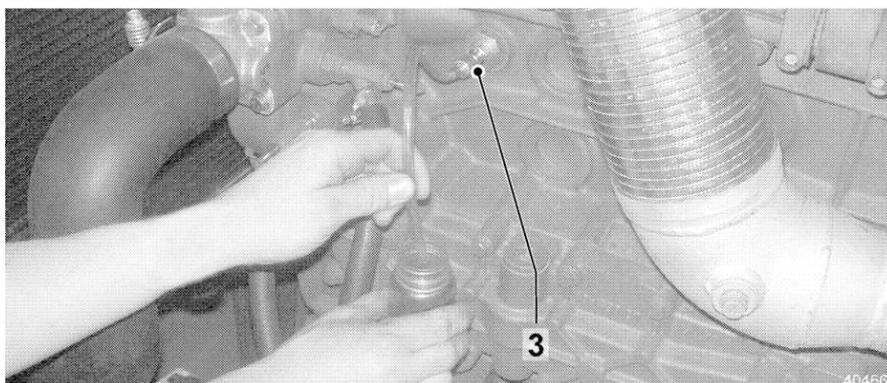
Kühlmittelentnahmeventil am Dieselmotor
